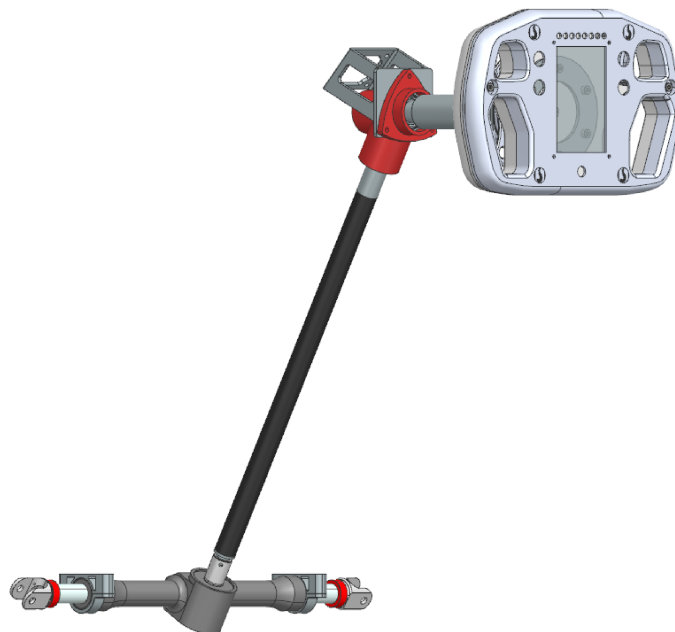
Assieme del sistema sterzante completo dei componenti montati a bordo della vettura (2)
